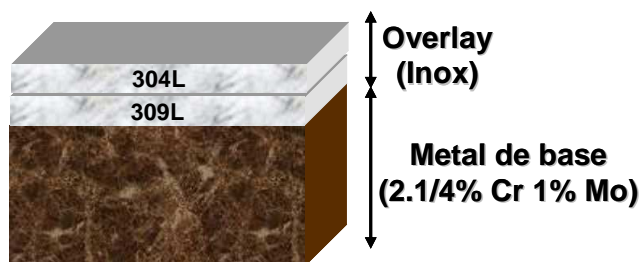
Figura esquemática da fabricação de um equipamento bimetálico.
